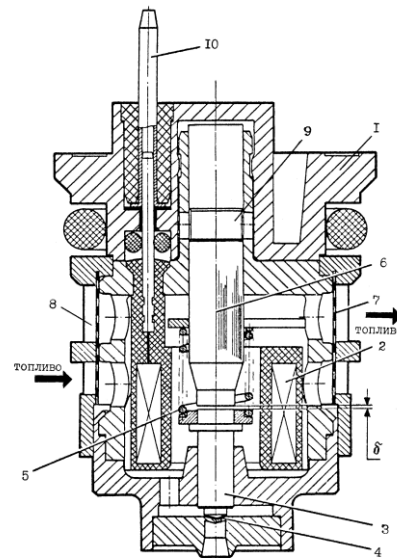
Конструкция форсунки с конусным запирающим элементом: 1 – корпус; 2 – обмотка электромагнита; 3 – запирающий элемент; 4 – канал распылителя; 5 – пружина; 6 – сердечник электромагнита; 7 – топливный фильтр (сетка); 8 – топливные каналы; 9 – регулировочный винт; 10 – электрические контакты
